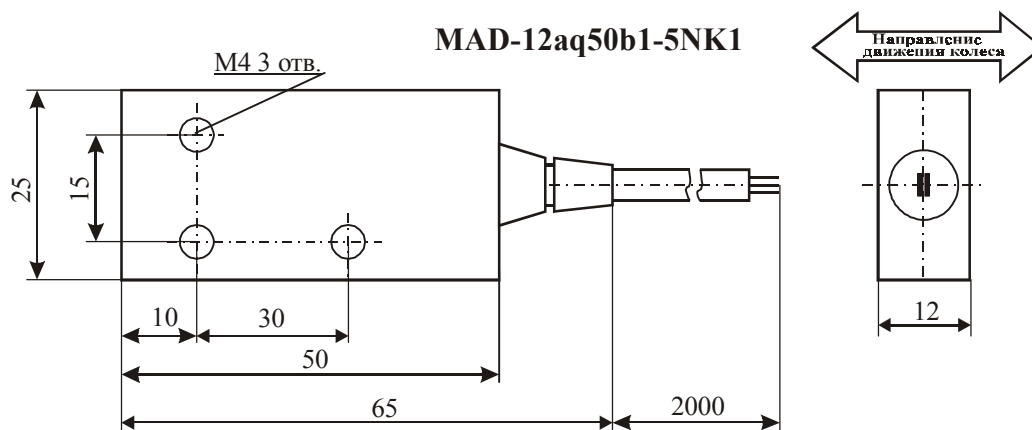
Внешний вид и габаритные размеры датчиков типа MAD-12aq
